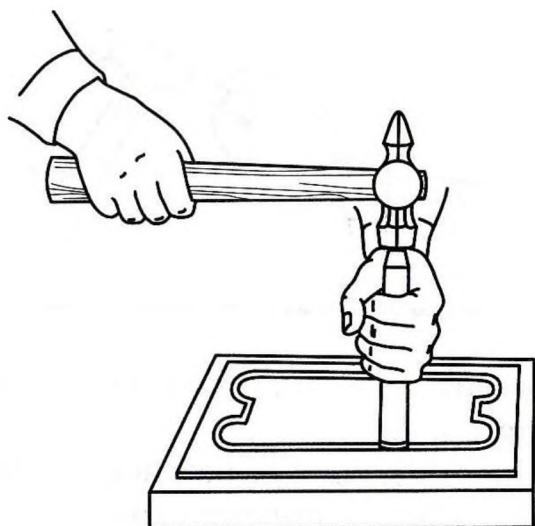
Вырубание из листового металла заготовки с криволинейным профилем.
